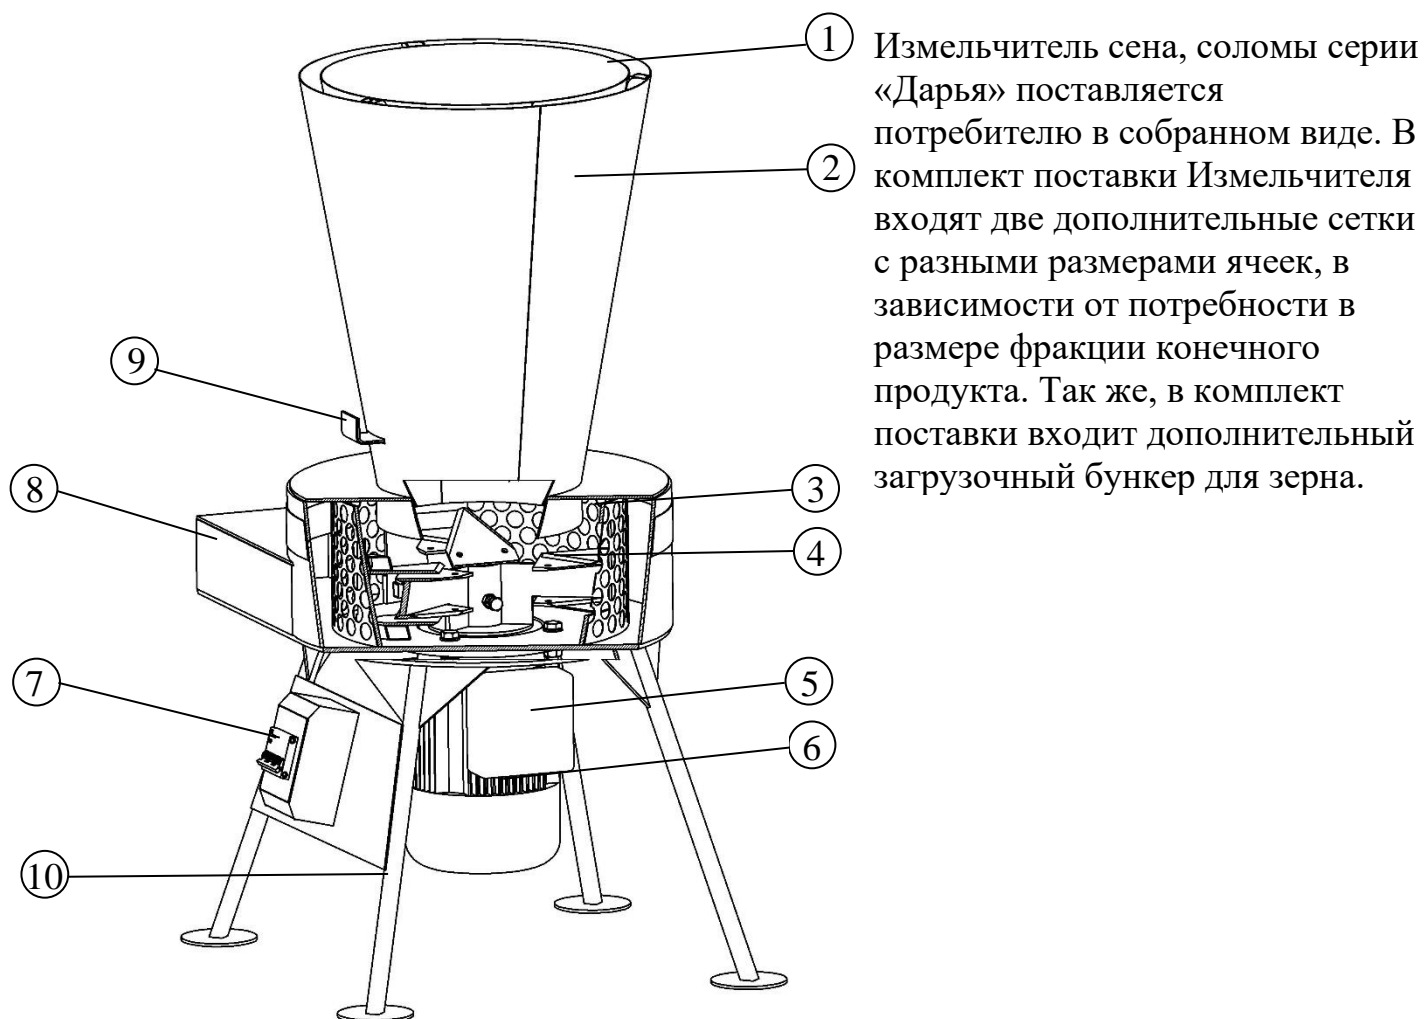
1-съемный загрузочный бункер для зерна, 2-основной загрузочный бункер, 3-сито, 4-режущие элементы, 5-коробка с пусковыми конденсаторами, 6-электродвигатель, 7-автоматический выключатель, 8-выходное отверстие, 9-дозирующая заслонка, 10-место маркировки изделия.
